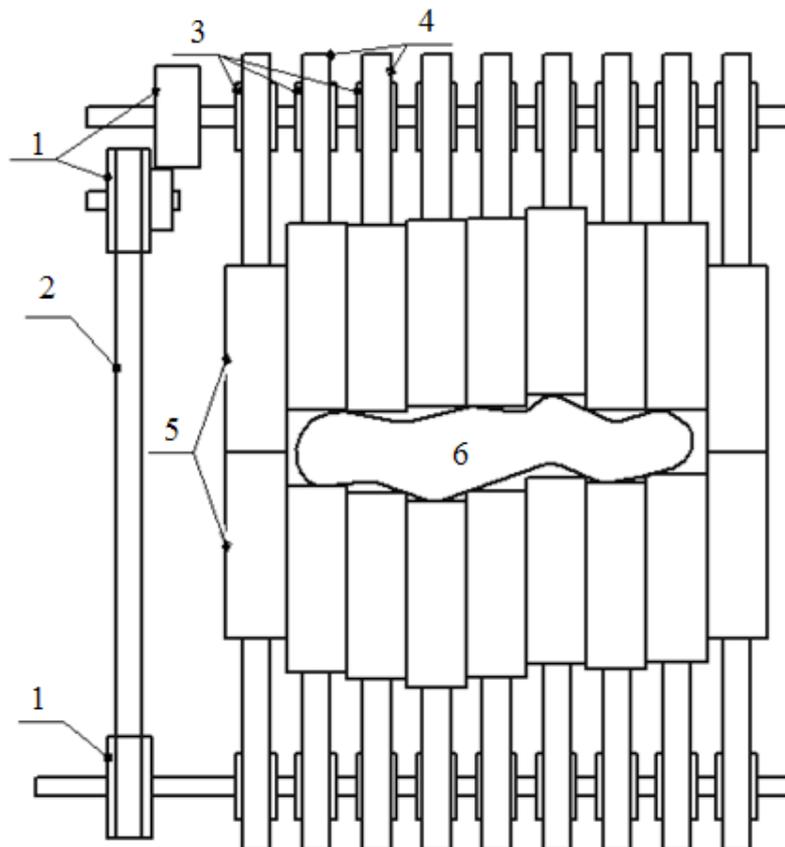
Схема МЛК: 1 — зубчатые колеса; 2 — ремень передачи; 3 — муфты приводов лепестков; 4 — зубчатые рейки; 5 — зубчатая рейка лепестка; 6 — заготовка, формирующая апертуру
